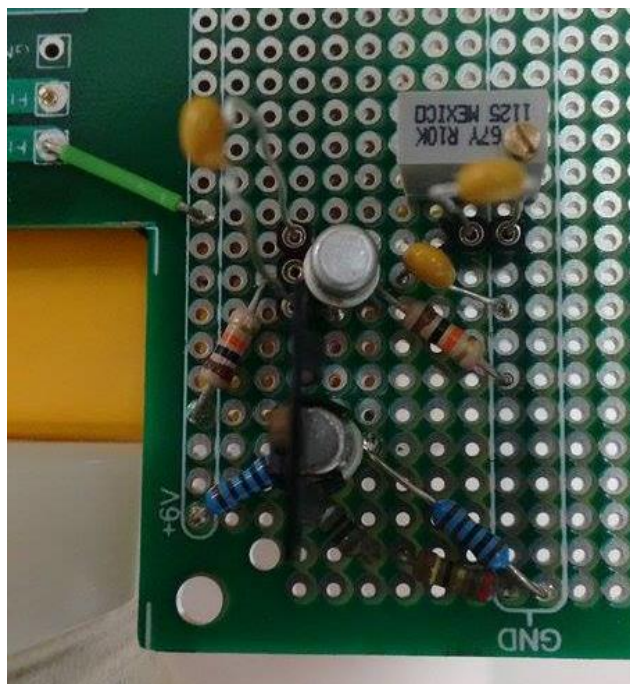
Circuito soldado diretamente em uma placa universal.
